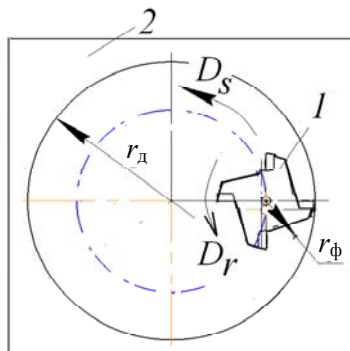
Схема обработки закрытой цилиндрической поверхности:
